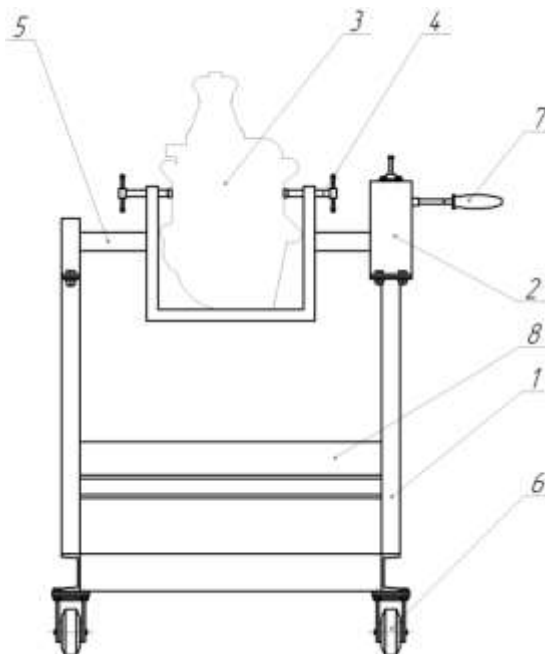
Разрабатываемый станд для сборки и разборки коробок перемены передач
